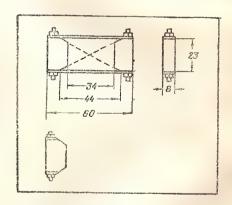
Разметна пакета и готовый башмак статора (снизу)
